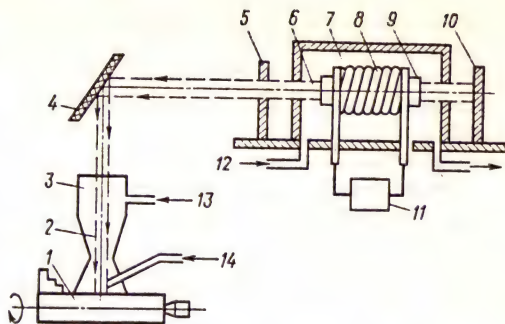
Схема установки для лазерной сварки и наплавки:
